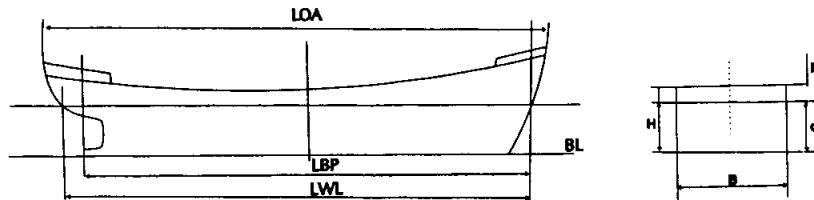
Principal Dimensions - Các kích thước chủ yếu
